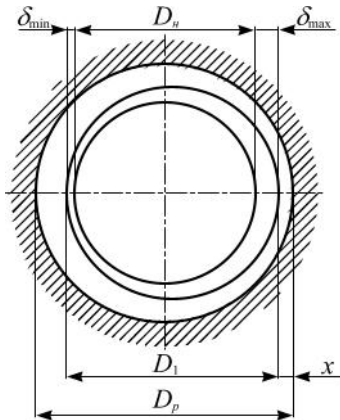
Схема спрацьованої поверхні отвору деталі, який розточується до ремонтного розміру
